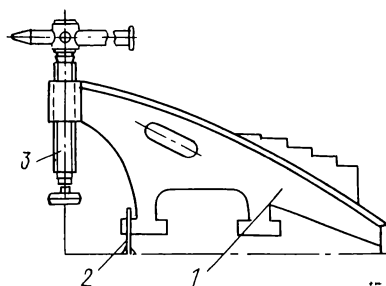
Рычажно-винтовое приспособление «рыбий хвост». 1 — рычаг; 2 — скоба; 3 — винт.
